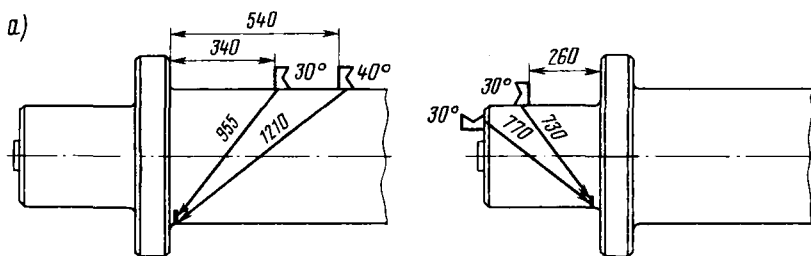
Схемы и зоны контроля главного приводного вала эскалатора Н-40М наклонными искателями со стороны левого торца
